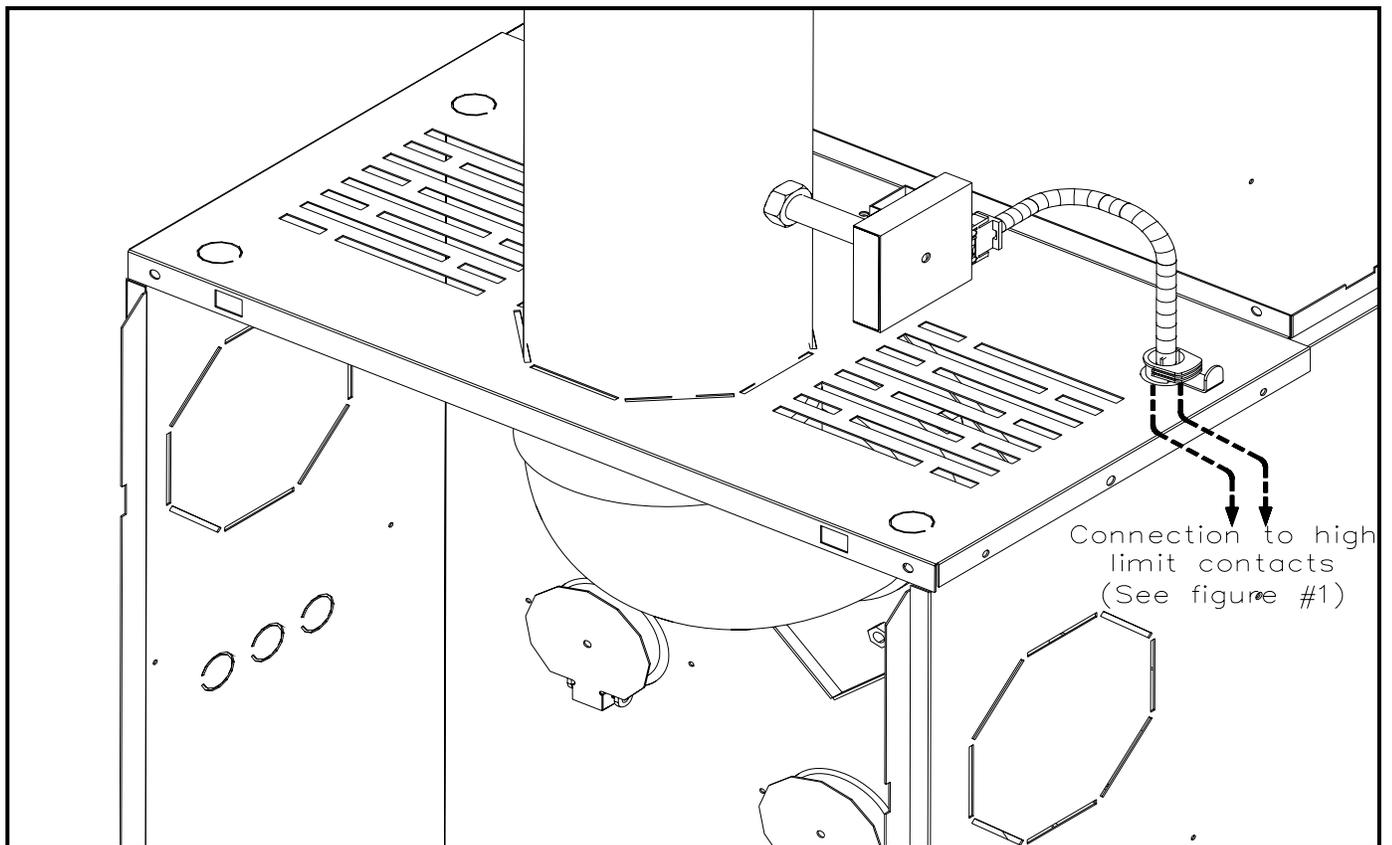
Arrangement général du système anti-refoulement, installation en débit d'air ascendant et évacuation horizontale
